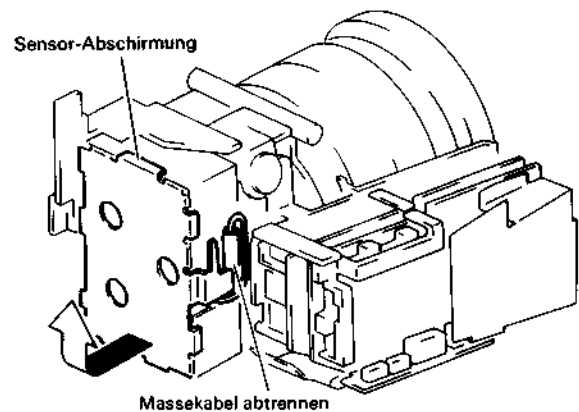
Ausbau der Sensor-Leiterplatte
